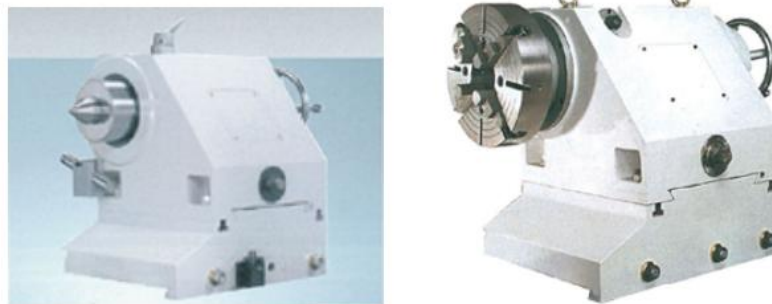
Hrotová bruska R/162 CNC 1000-7000
